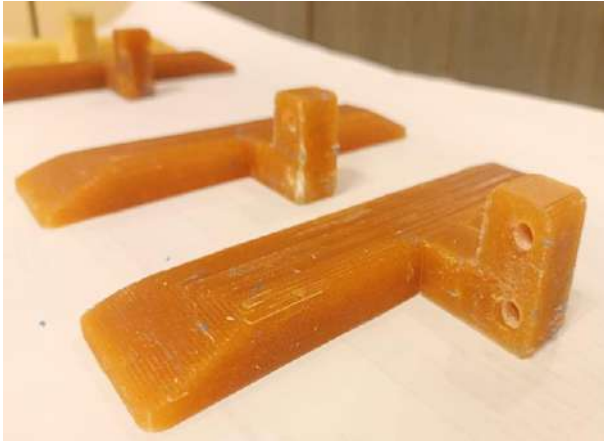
Лопатка конвейера после изготовления из древесно-полимерного композита двухэкструдерным 3D-принтером
